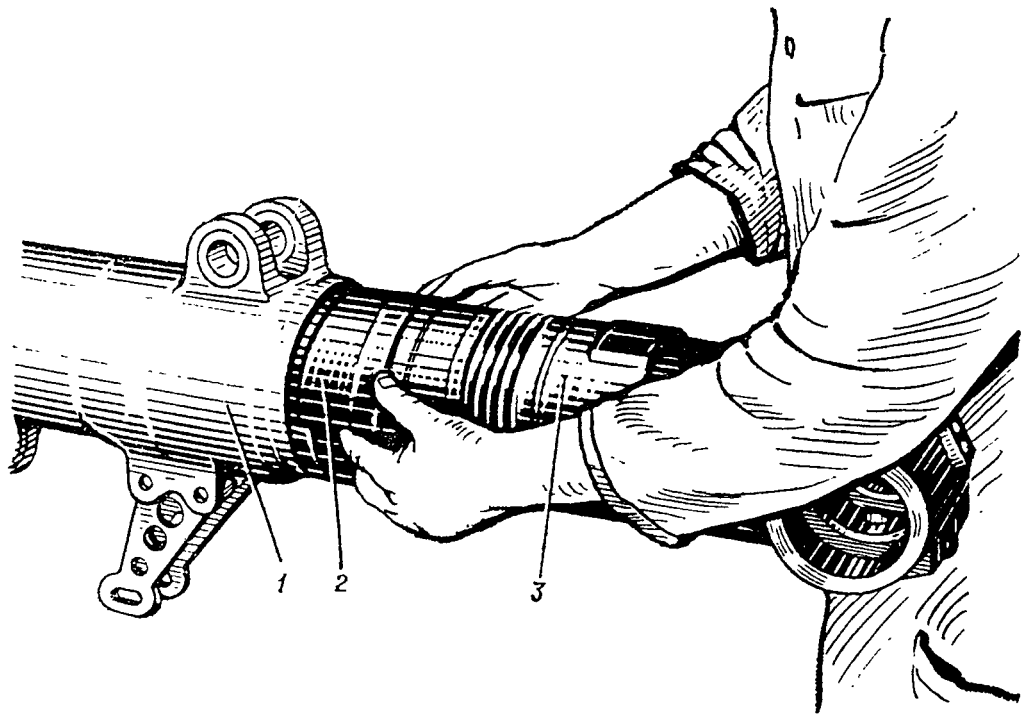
Установка в цилиндр разъемной оправки 6-1600/Д-44.
